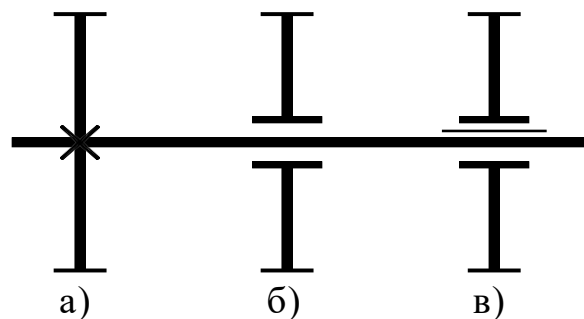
Умовні позначки установки зубчастих коліс на валах
